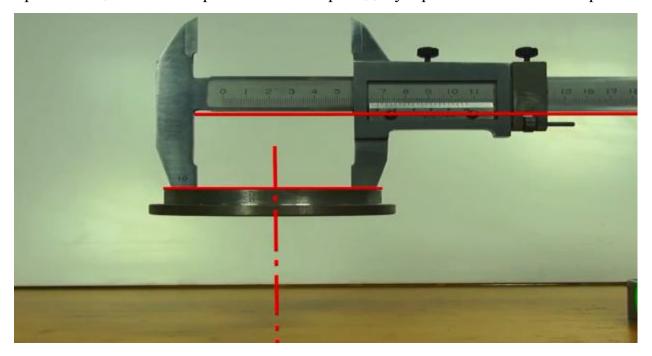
Положение штангенциркуля при измерениях цилиндрических отверстий
